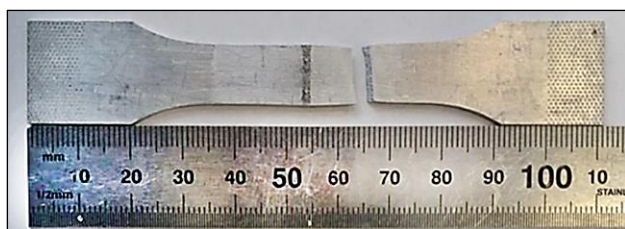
Образец со сварным соединением после мех. испытаний. Разрыв по основному материалу.
